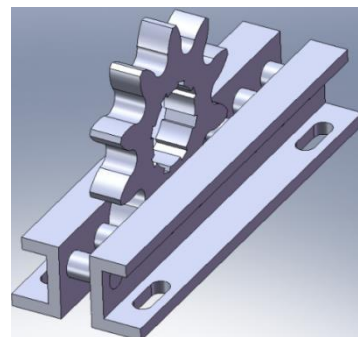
Конструктивный вариант зубчато-реечной передачи для перемещения шахтного электровоза
